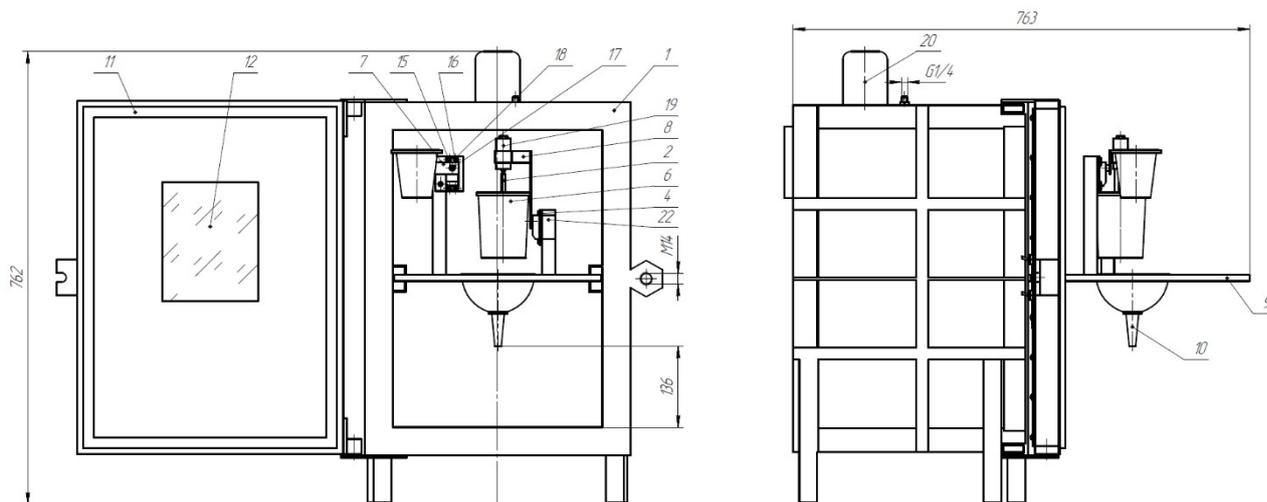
Сборочный чертеж автоматизированной установки для мелкосерийного литья
